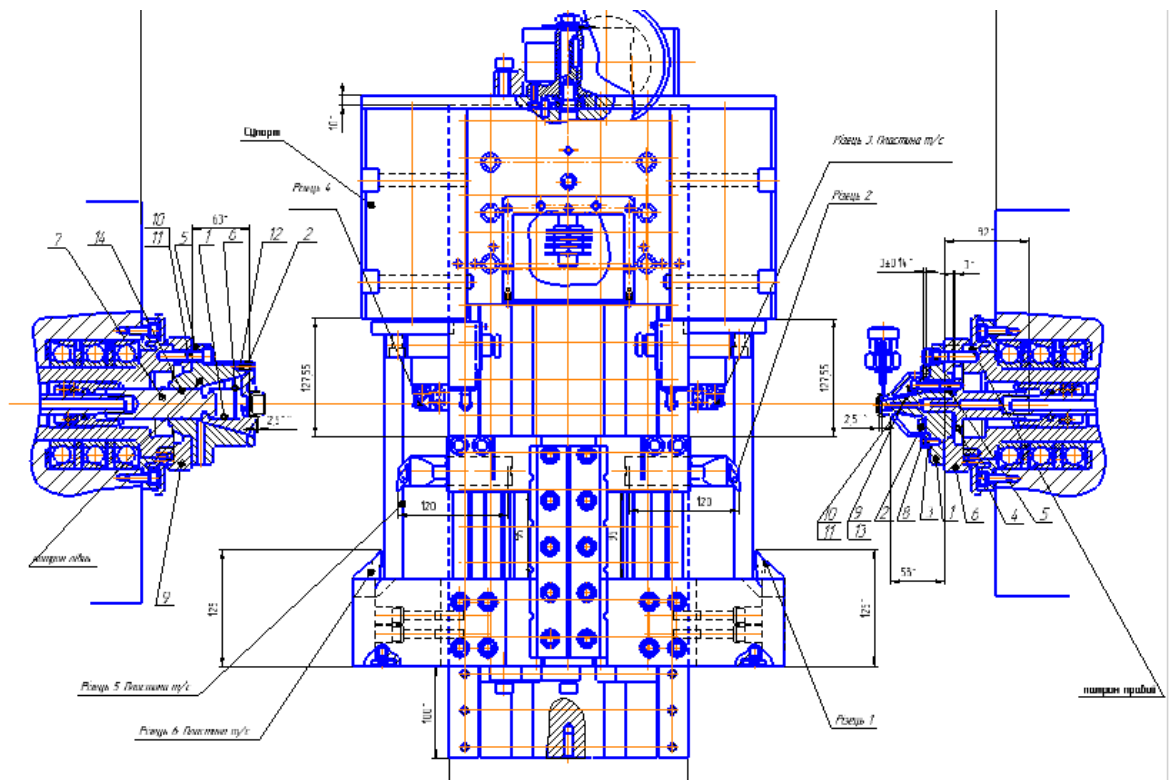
Розташування інструментального забезпечення на хрестовому супорті верстата
